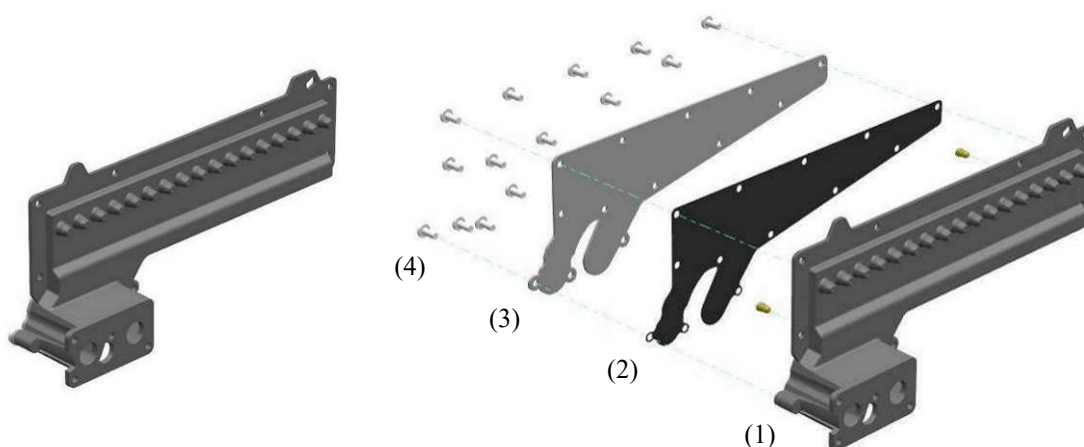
Corpo em alumínio injetado e maquinado (conjunto montado e conjunto explodido)
